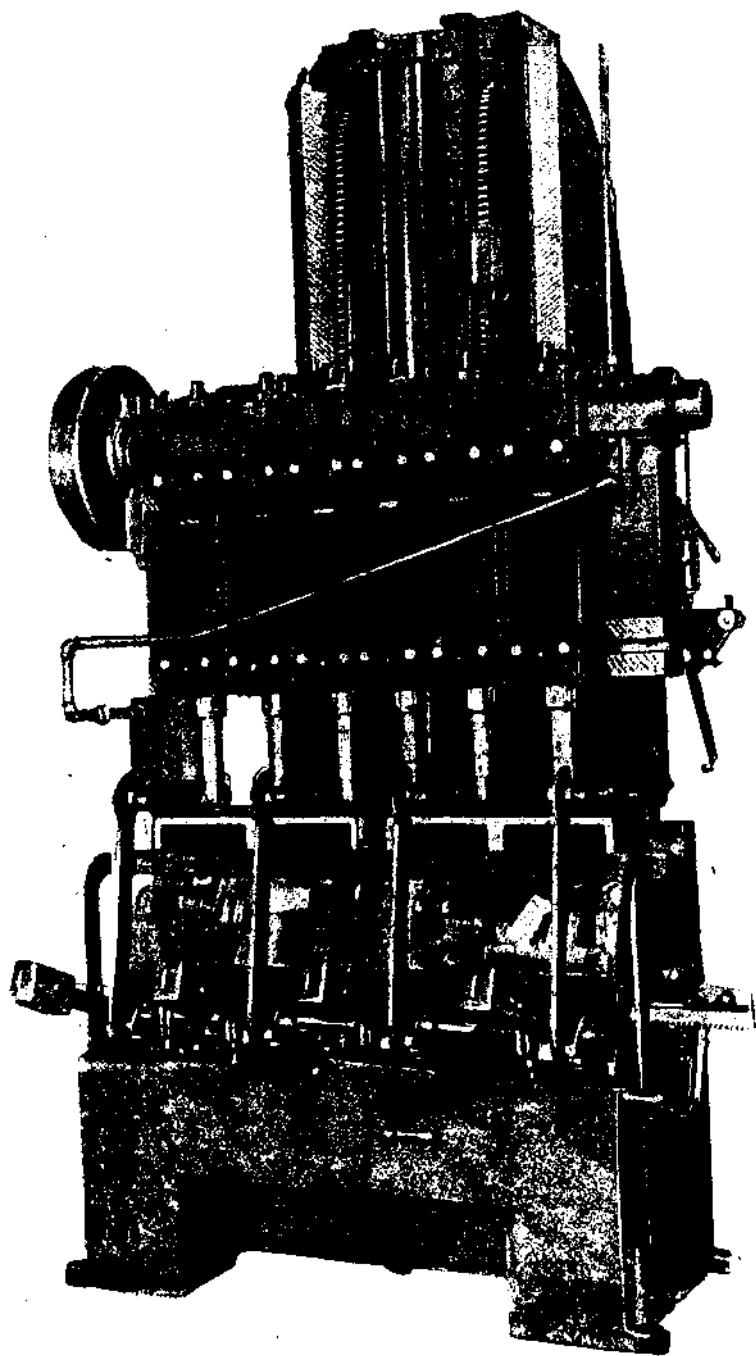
Станок Moline Tool Co для работы без нижних направляющих.
